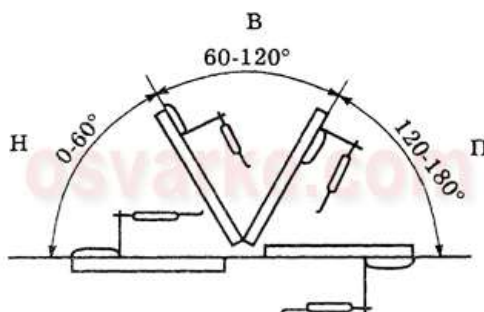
Положения изделия при ручной дуговой сварке
